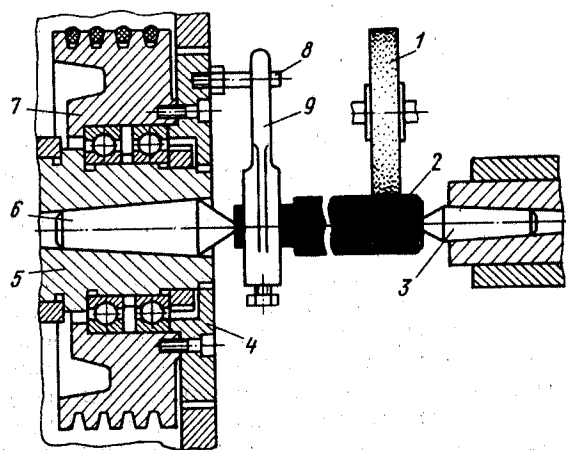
Установка заготовки в неподвижных центрах круглошлифовального станка
